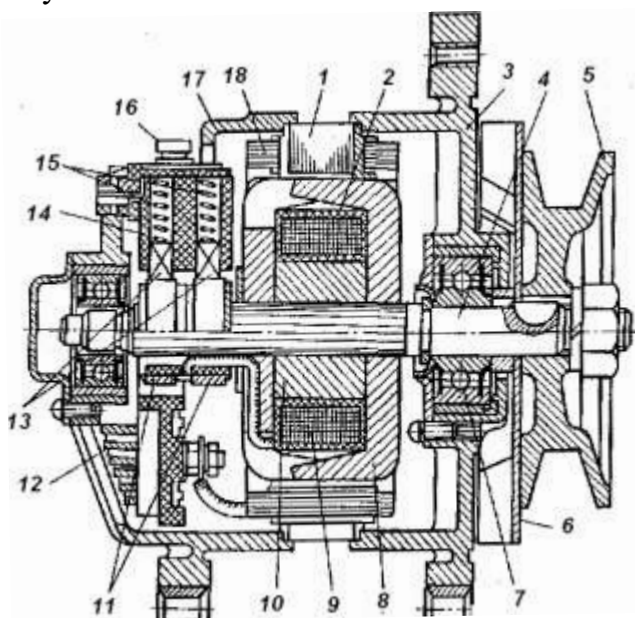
Генератор переменного тока Г250-И: 1 - статор; 2 - ротор; 3 - передняя крышка; 4 - вал; 5 - приводной шкив; 6 - вентилятор; 7 - шариковый подшипник; 8 - наконечник ротора; 9 - обмотка возбуждения; 10 - втулка; 11 - медные контактные кольца; 12 - радиатор выпрямительного блока; 13 - щетки; 14 - щеткодержатель; 15 - пружины щеток; 16 - выводной зажим; 17 - задняя крышка; 18 - обмотка статора.
